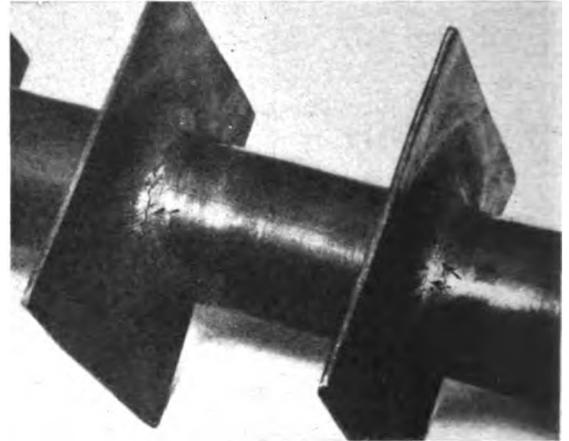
Schweißrisse an einem Stahlrohr.
